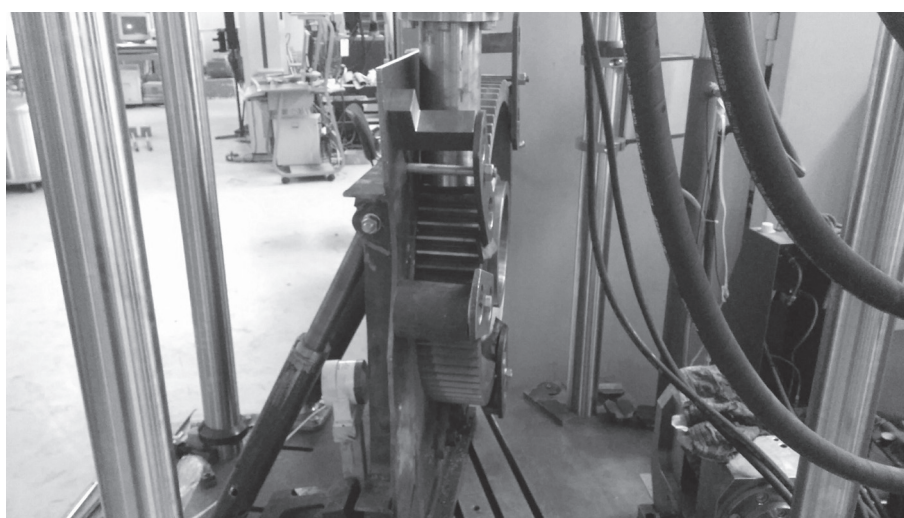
Испытание зуба косозубого (а) и прямозубого (б) зубчатого колеса на изгиб
